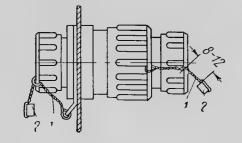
Контровка штепсельных разъемов типа ШРН (вид контровки 8): 1 — проволока; 2 — пломба
